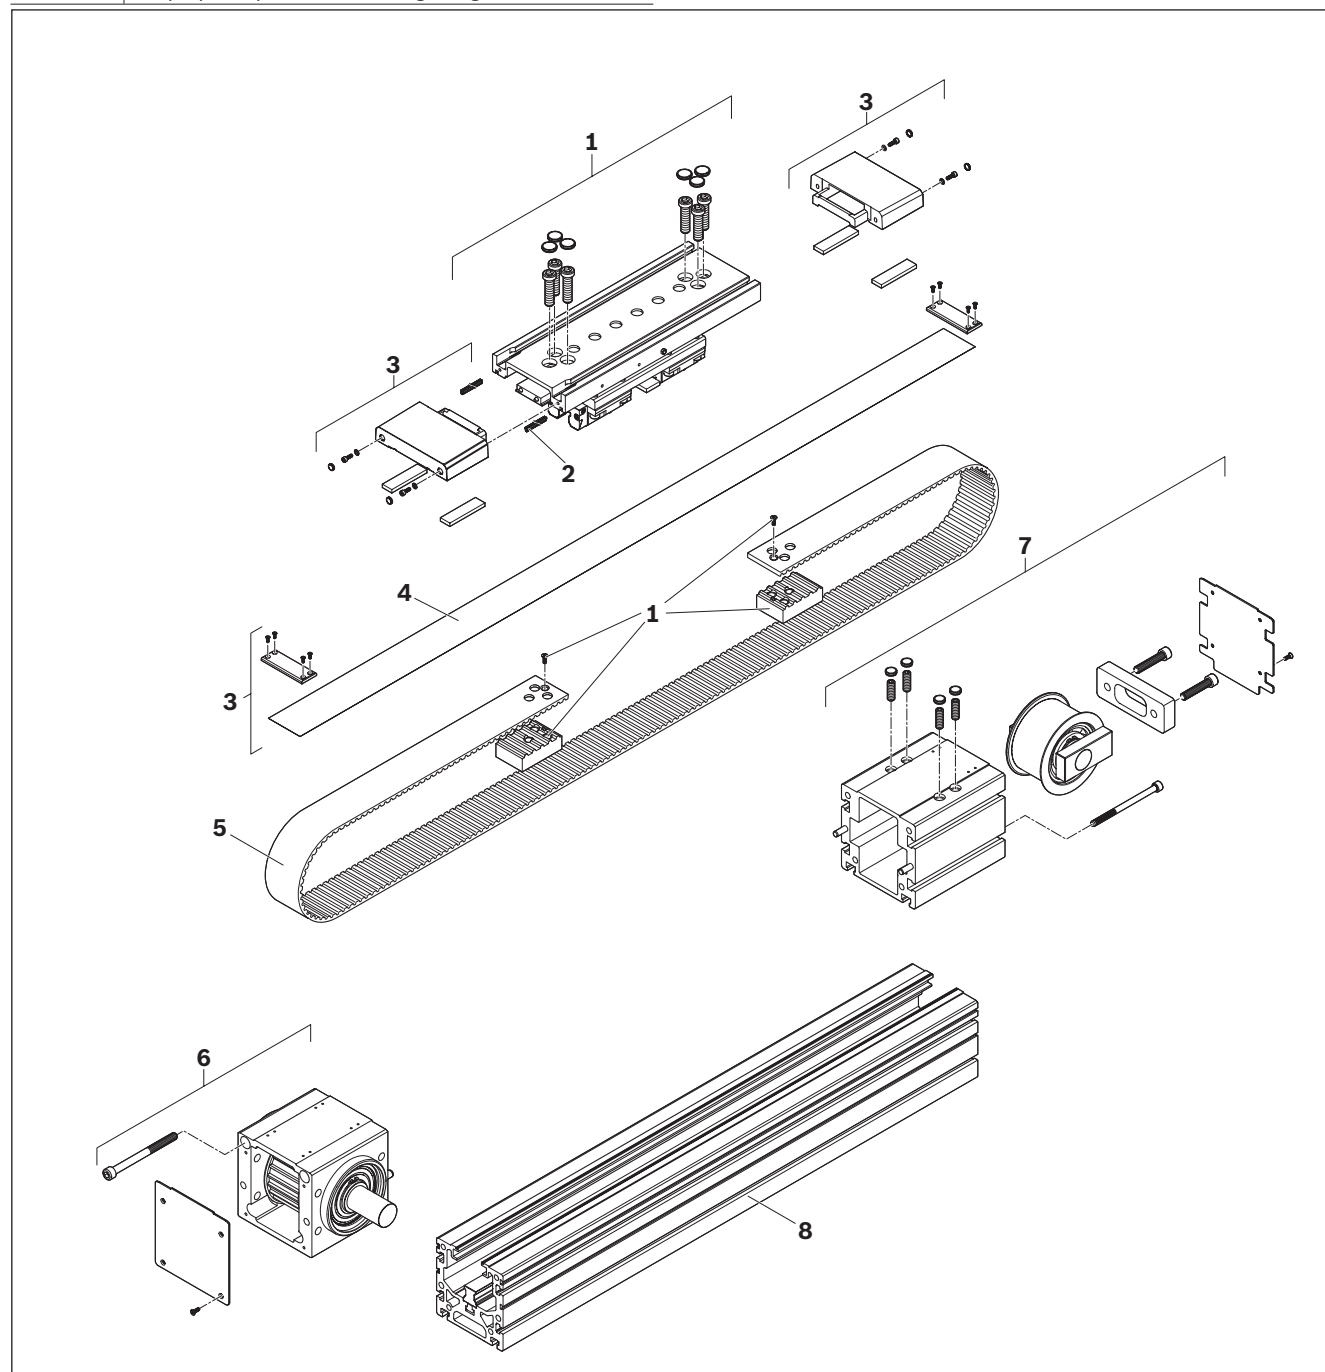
Vue d'ensemble MKR-065/-080/-110/-140-NN-3
